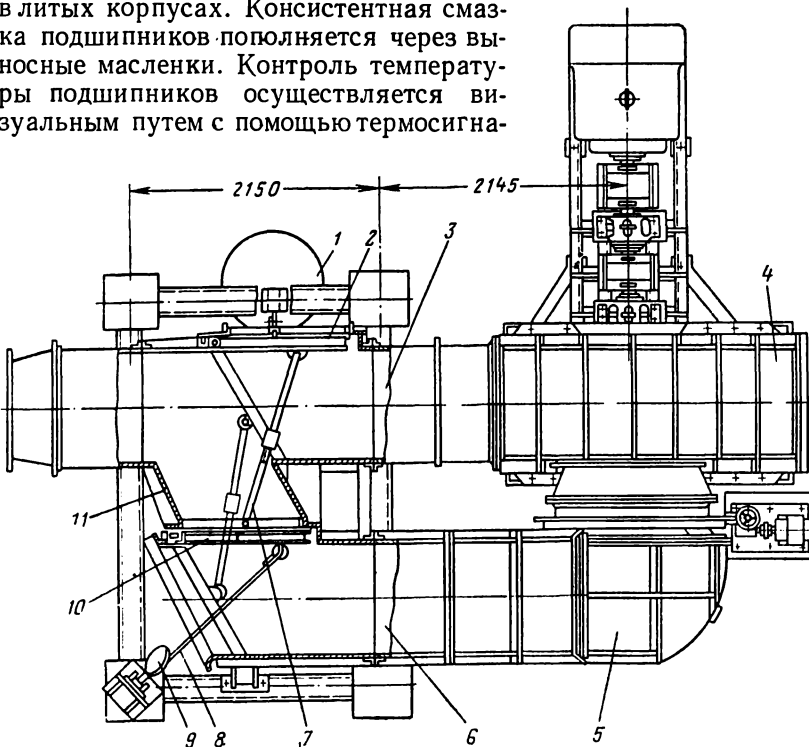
Вентилятор ВЦП-16 с реверсивным устройством
